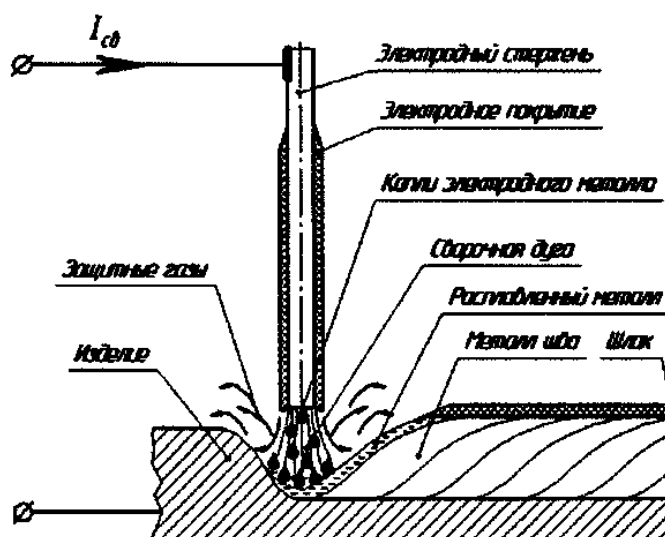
Схема сварки покрытым металлическим электродом
